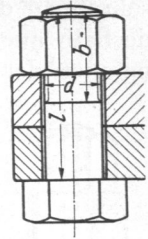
Schraube mit Mutter oder Durchsteckschraube.
